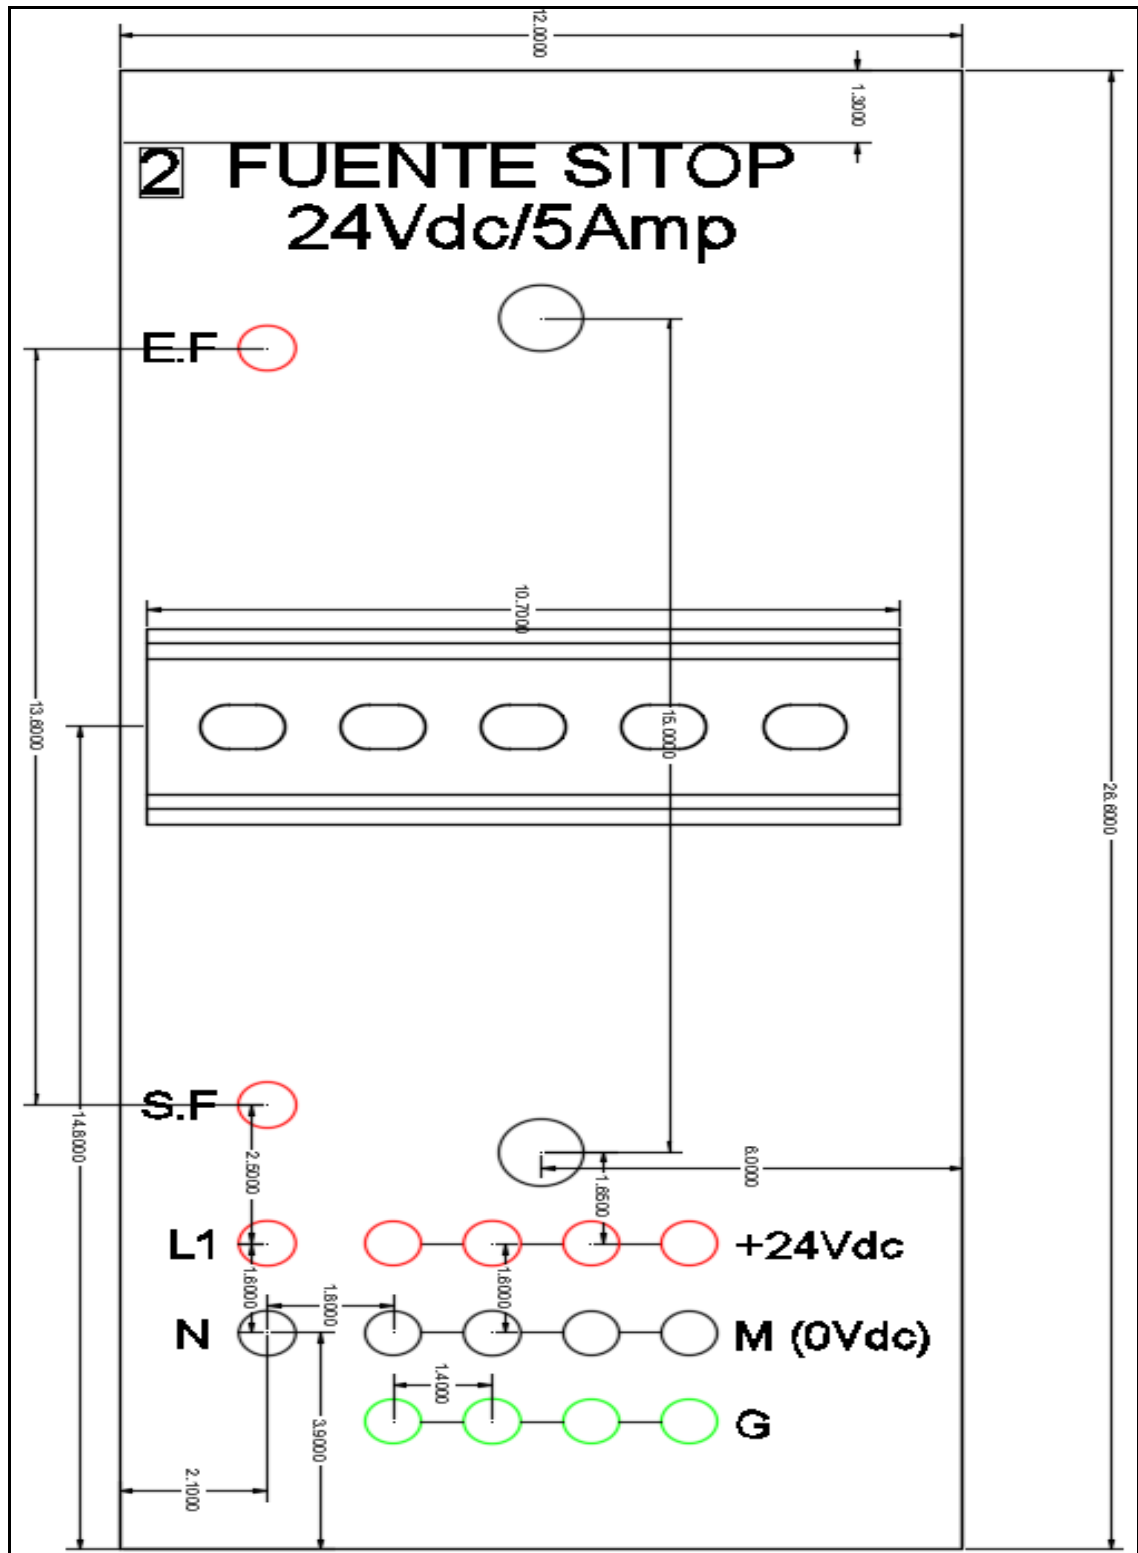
Plano de la lámina deslizante de fuente SITOP.
